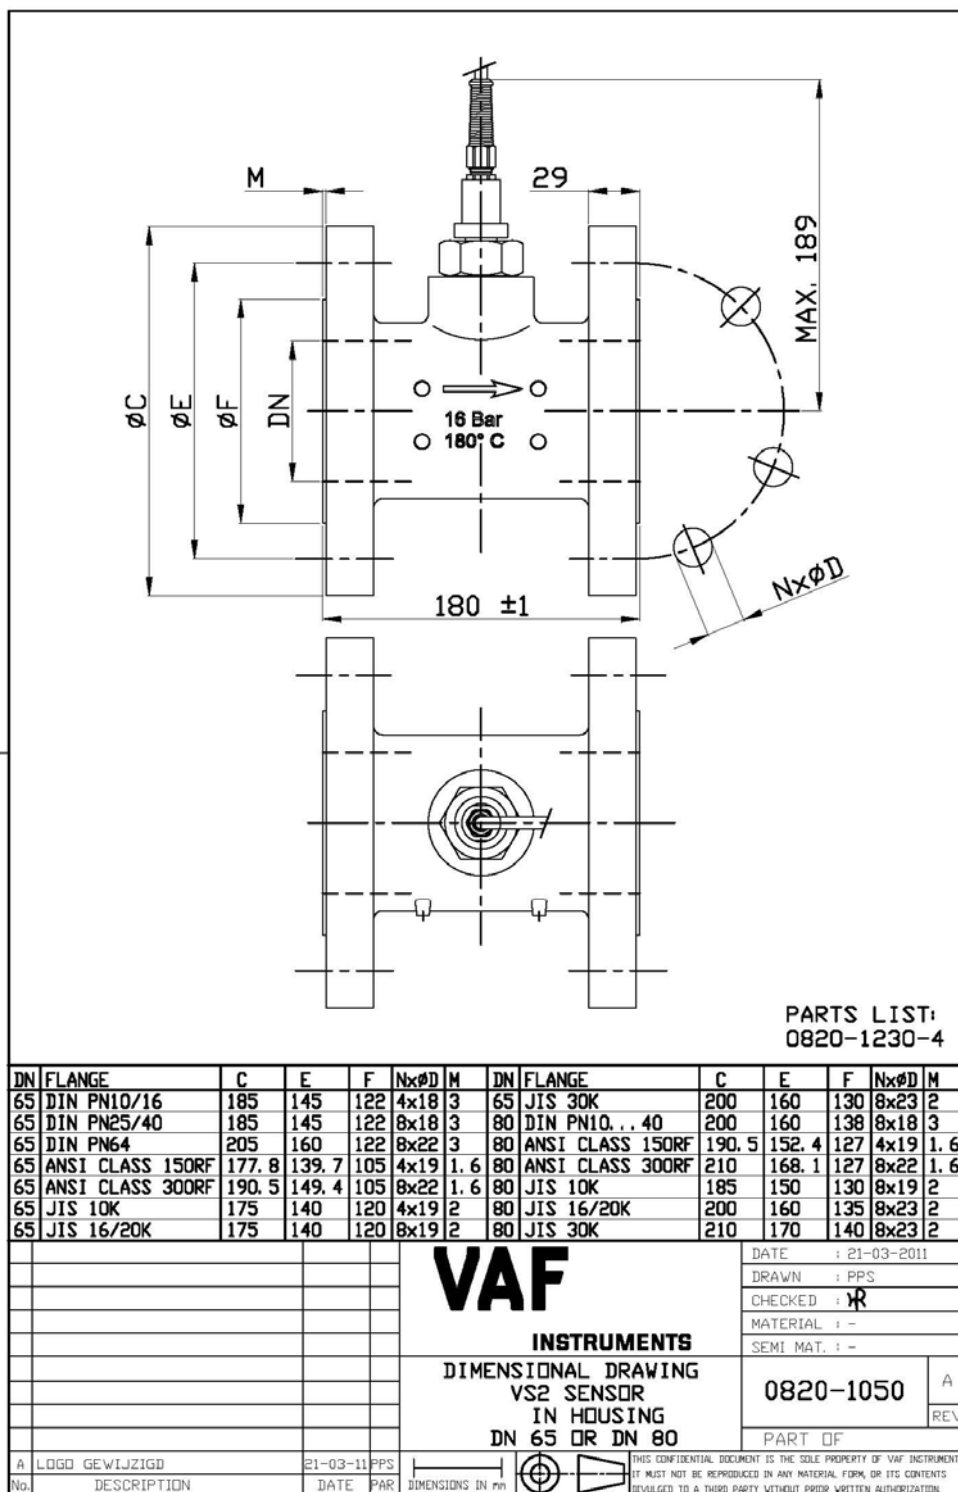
Dimensioni del sensore ViscoSense®2 (Tutte le dimensioni sono in millimetri).
